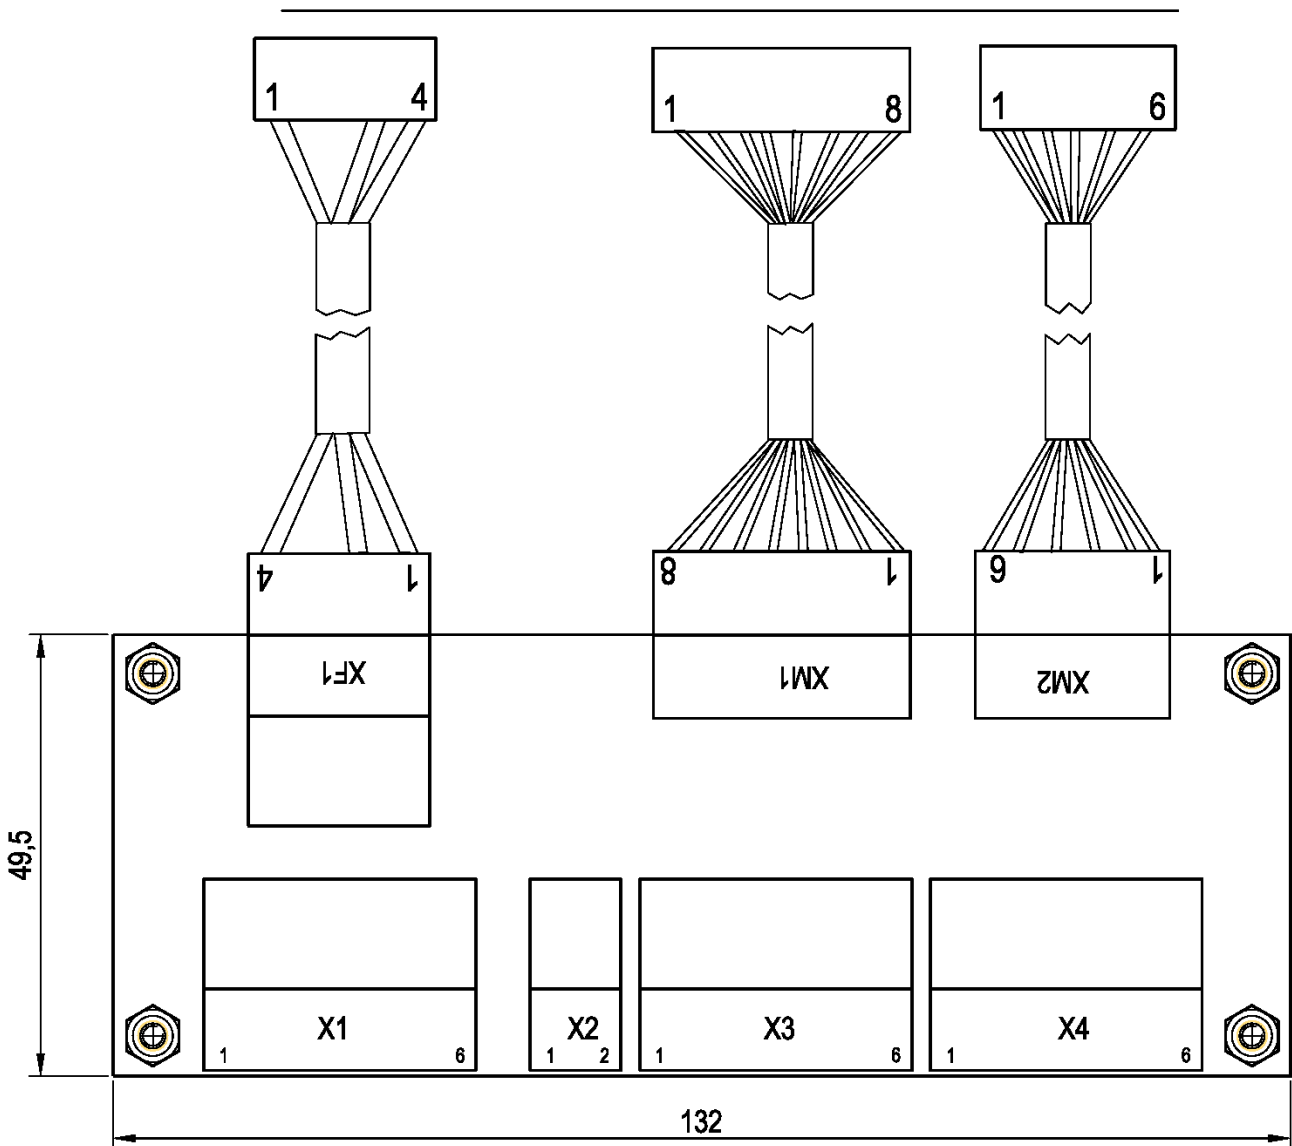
Внешний вид и габаритные размеры КРАБ-2.
